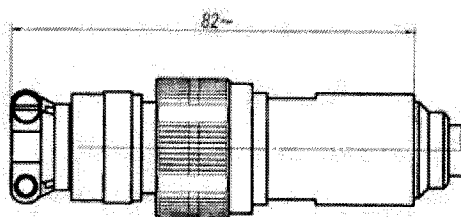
Кресленик зовнішньої частини ТХА-1090, ТХК-1090 з головою
